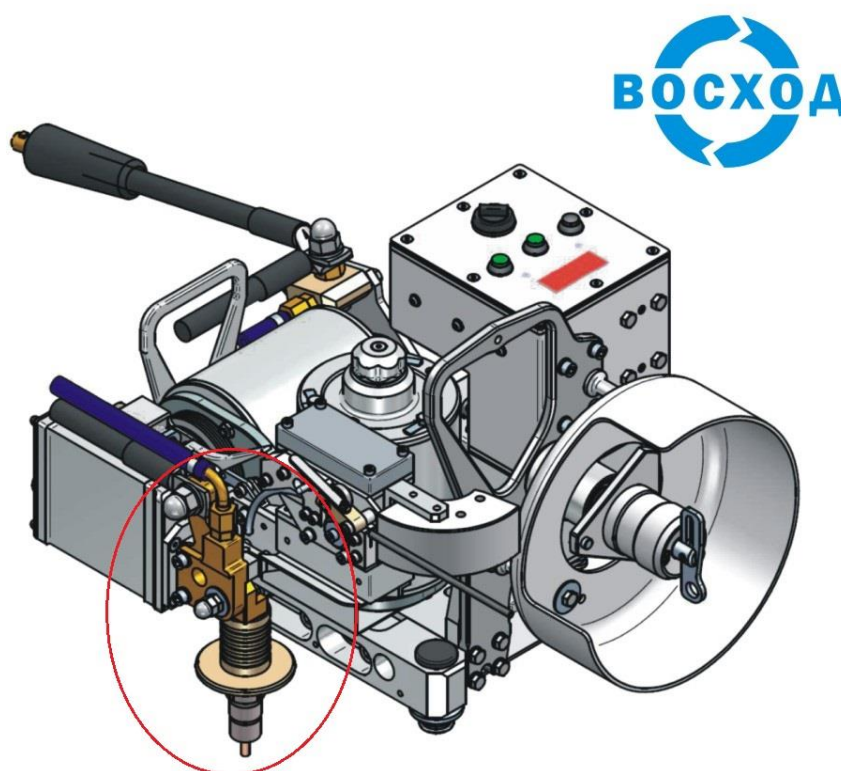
комплекс для автоматической сварки «Восход».
